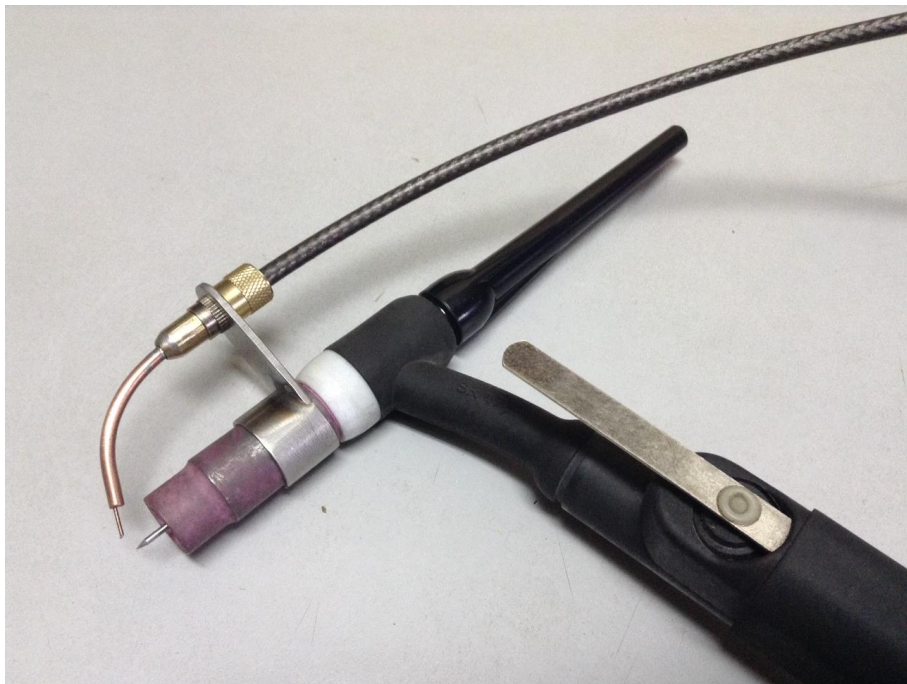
Горелка для механизированной сварки неплавящимся электродом
